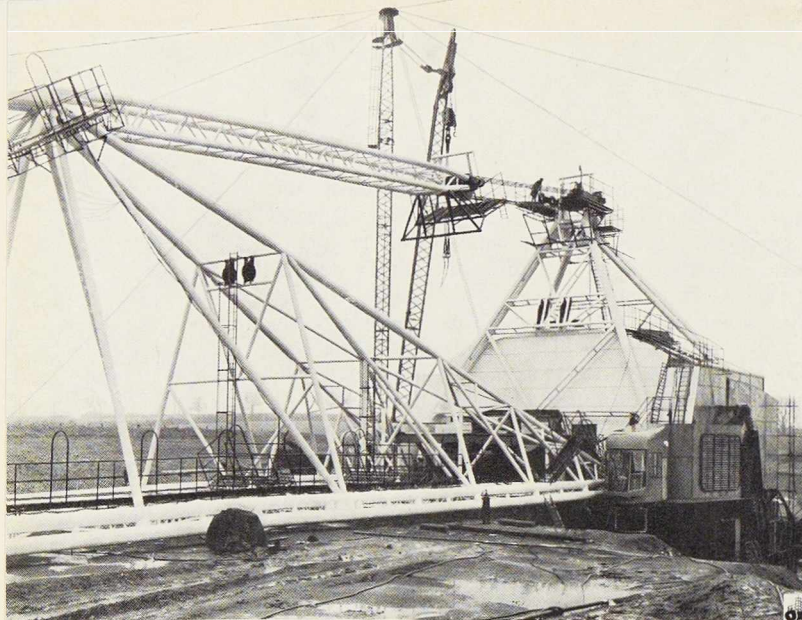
Montage de la flèche en tubes soudés sur l'engin.
